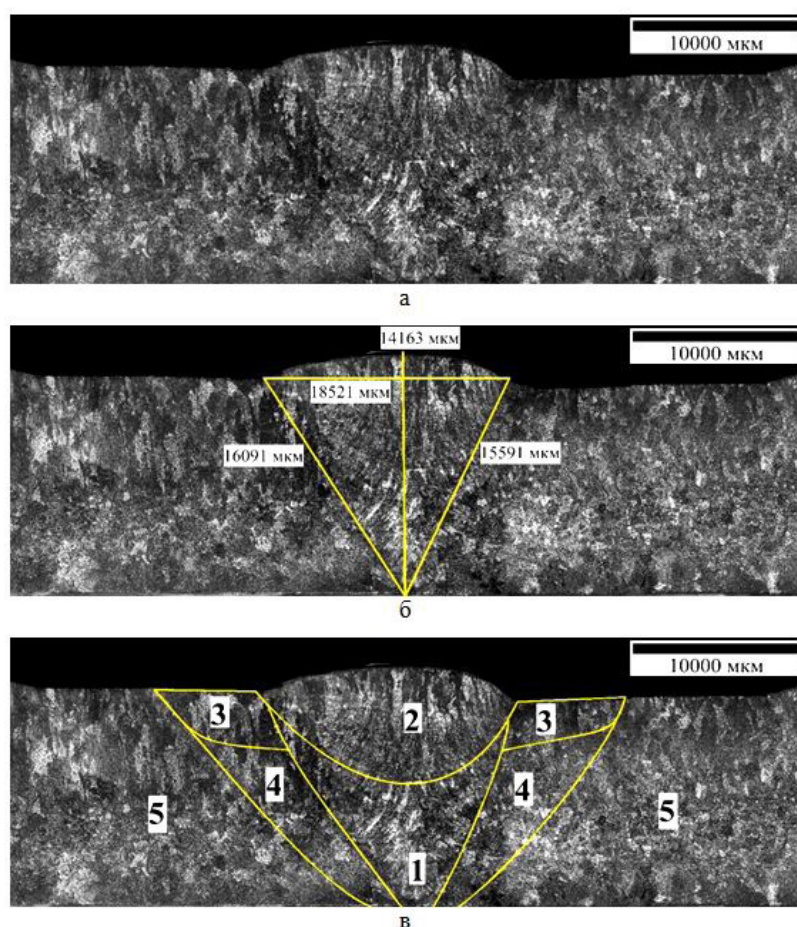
Макроструктура сплава в поперечном сечении трубного сварного соединения: а – общий вид; б – вид с размерами металла шва; в – вид с выделенными границами различных участков сварного соединения: 1 – первый (корневой) валик, 2 – второй валик, 3 – участок усиления шва, 4 – зона термического влияния, 5 – основной металл
